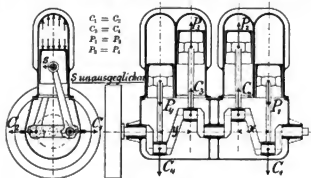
Zwillingmotor mit gleichgerichteten Kurbeln.
